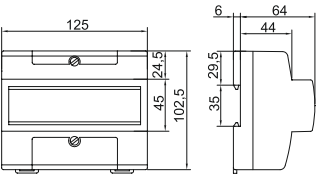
Габаритные и присоединительные размеры счётчиков габарита корпуса 2
